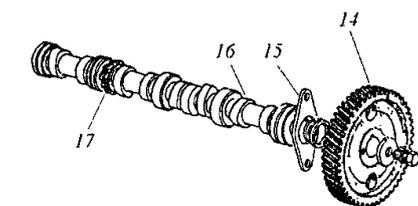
Газораспределительный механизм двигателя ЗМЗ-4025.10
